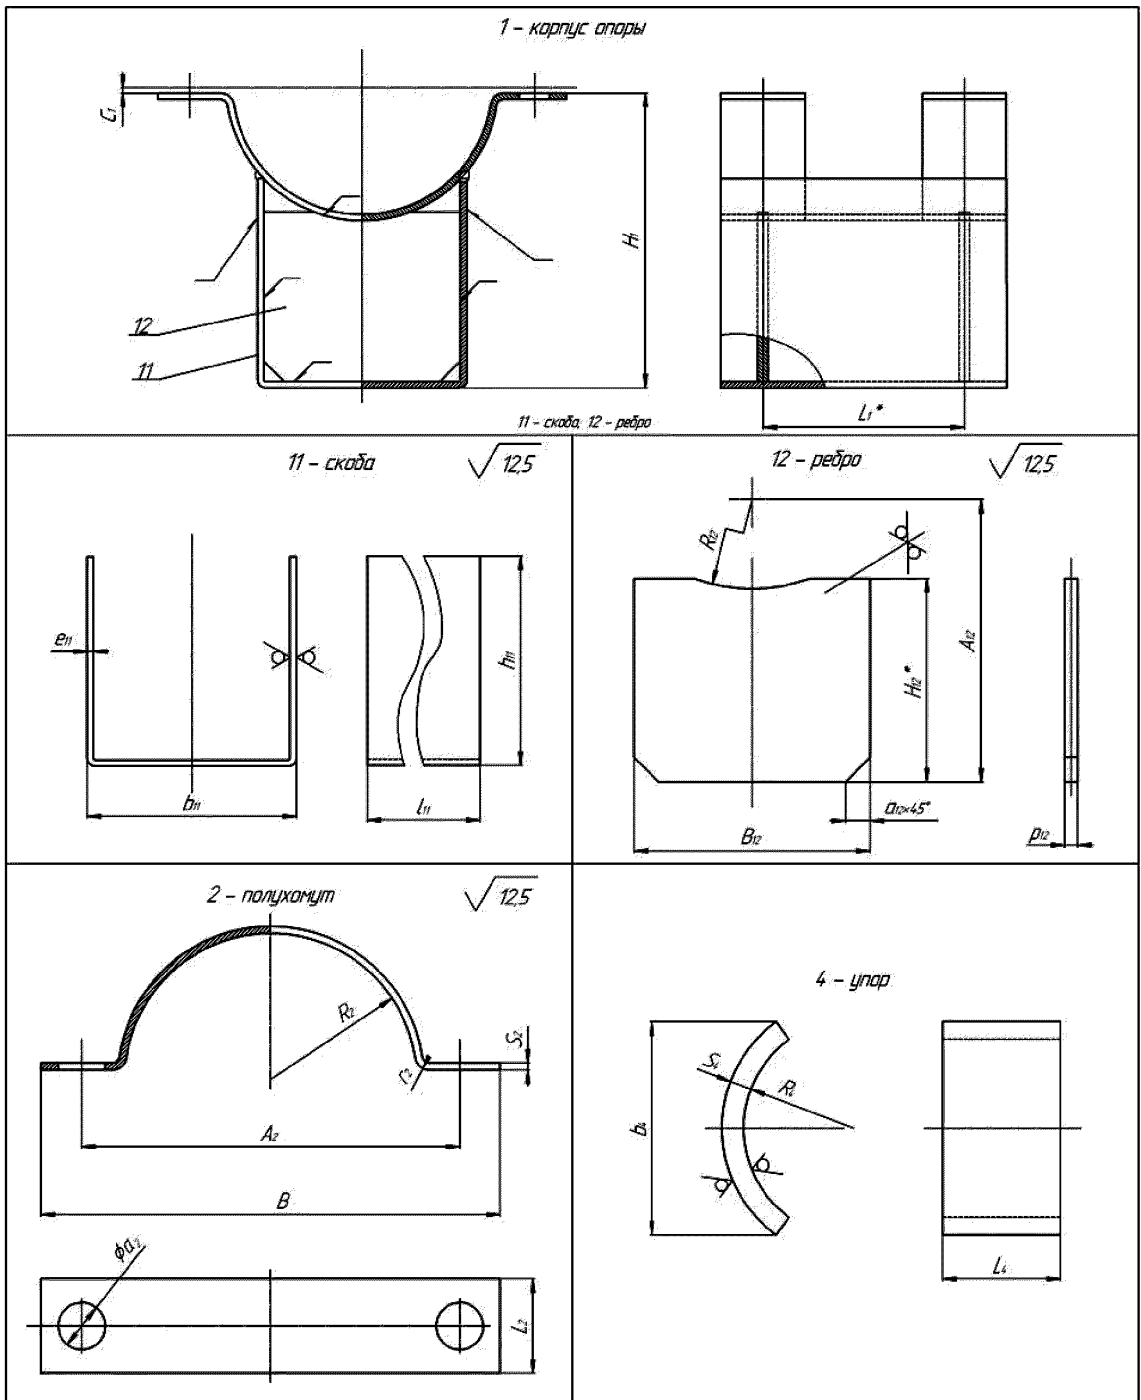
Детали изделий 0101-XXXX-F-1C-03-A,
